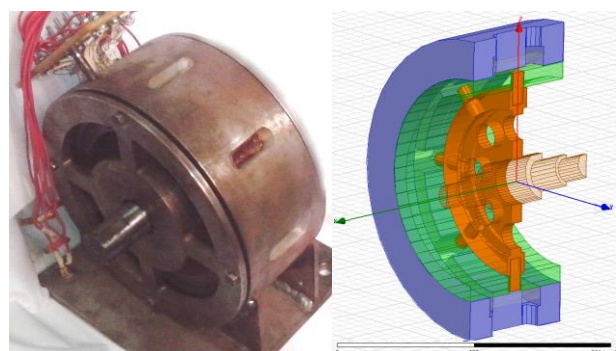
Конструкція 8-пазового ДРК з габаритними розмірами 250x250x100 мм
